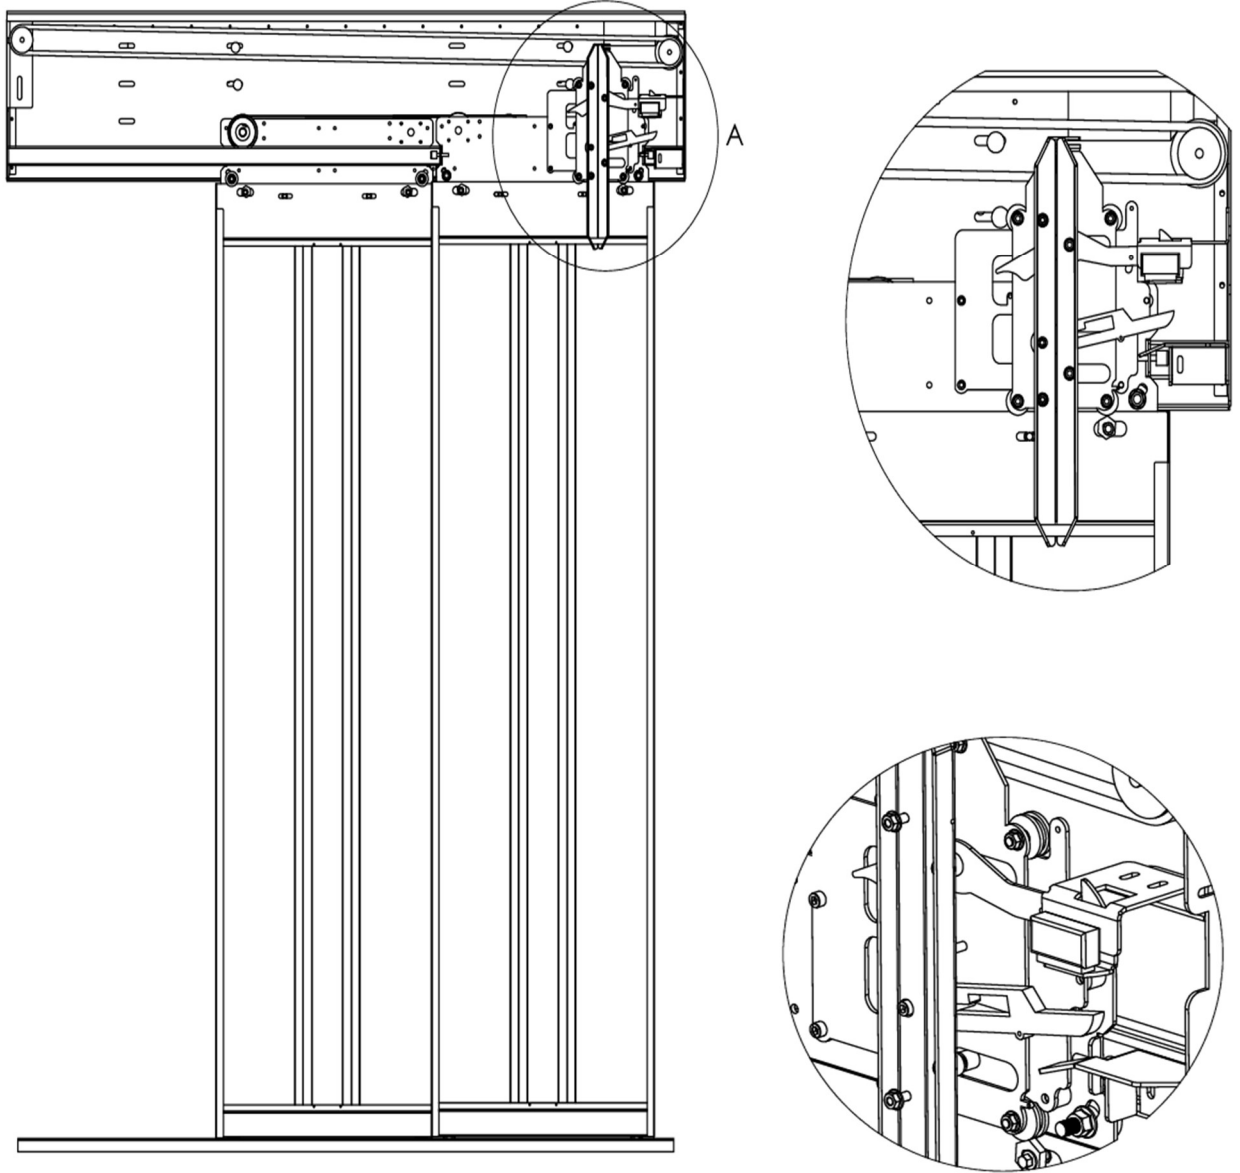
Kabin Mekanizmasının Tavana Montajı
